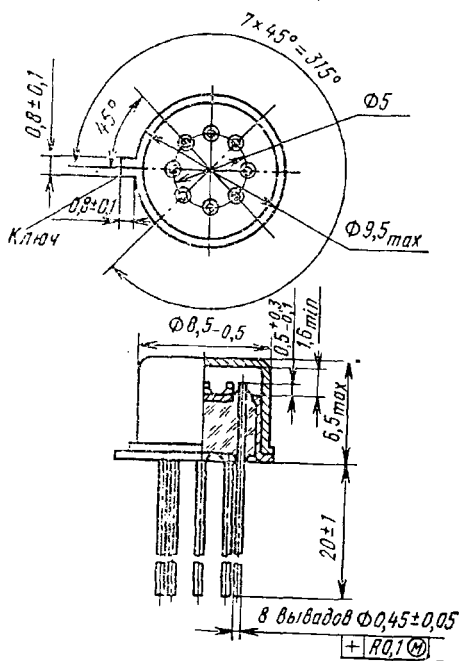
Конструкция металлокерамического корпуса 3104 (302.8-1)
